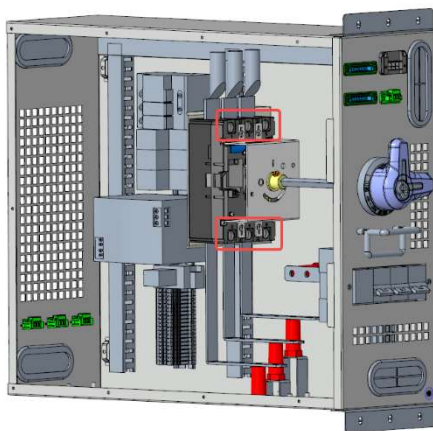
Remova o barramento de cobre e o cabo conectados ao disjuntor
